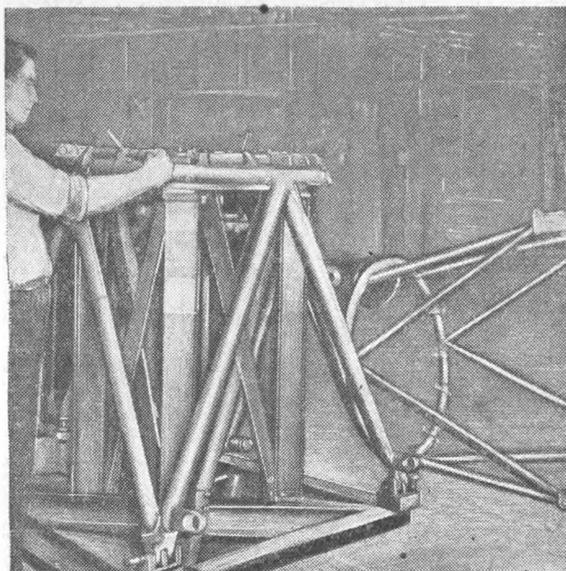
Разделочный стапель для расточки и развертки стыковочных отверстий при помощи сверлильных головок.
